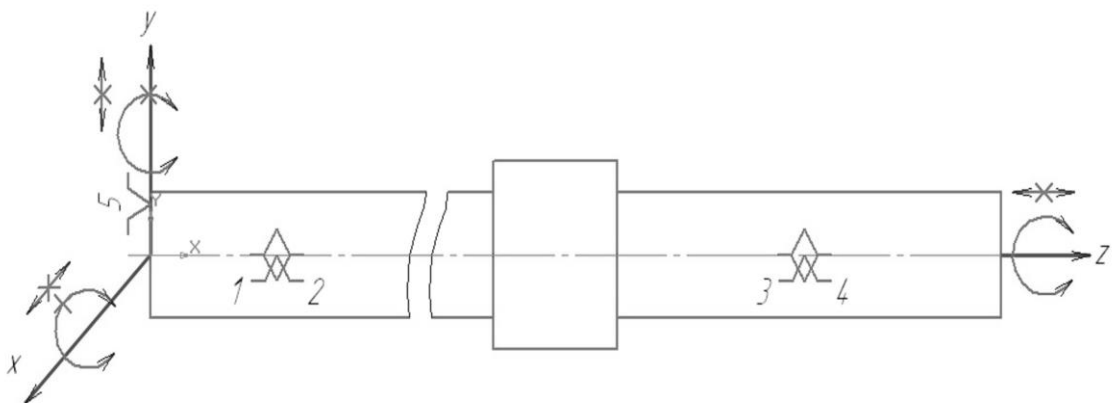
Схема базування заготовки на 010, 015, 025, 035,040 операції
